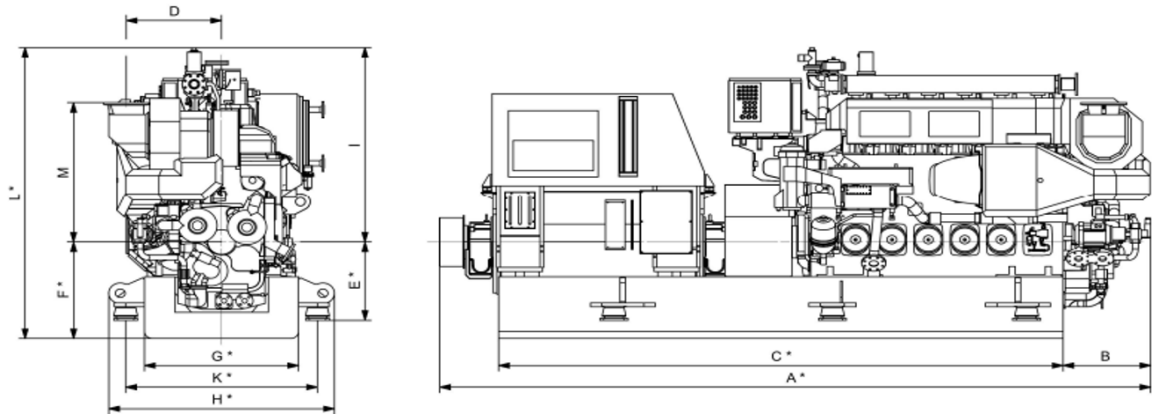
Dimensiones del motor Wärtsilä 6L20DF.
